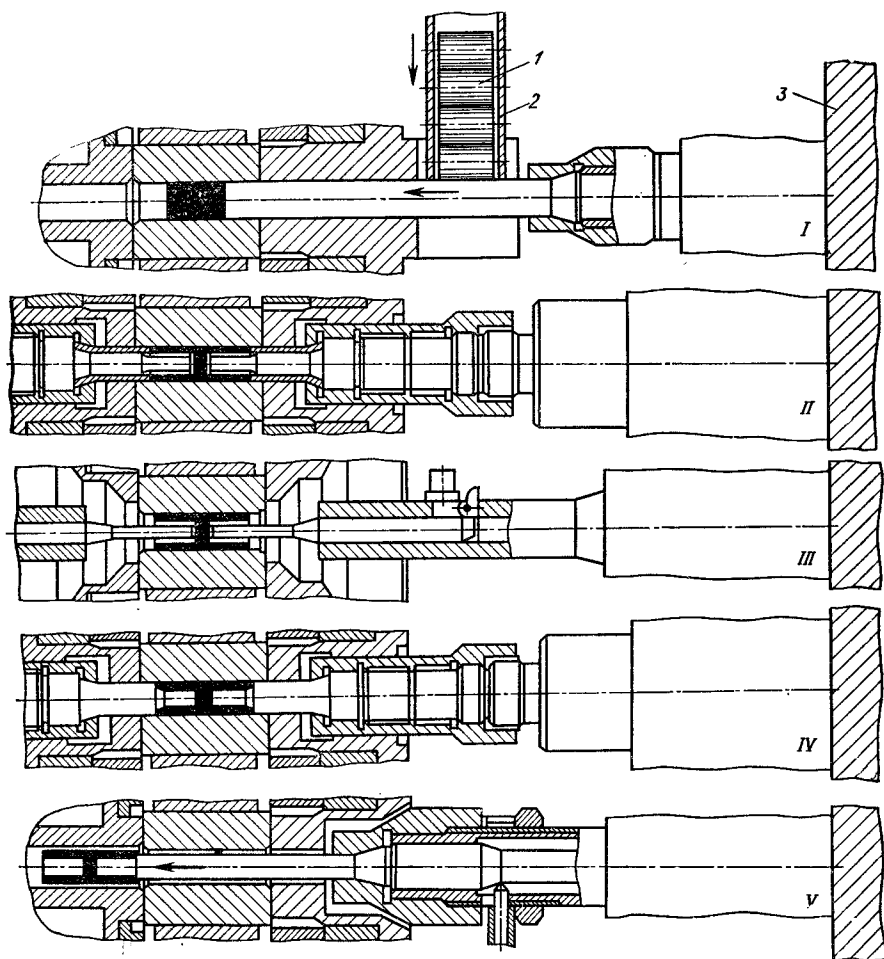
Штамповочный инструмент и процесс формообразования поршневых пальцев
